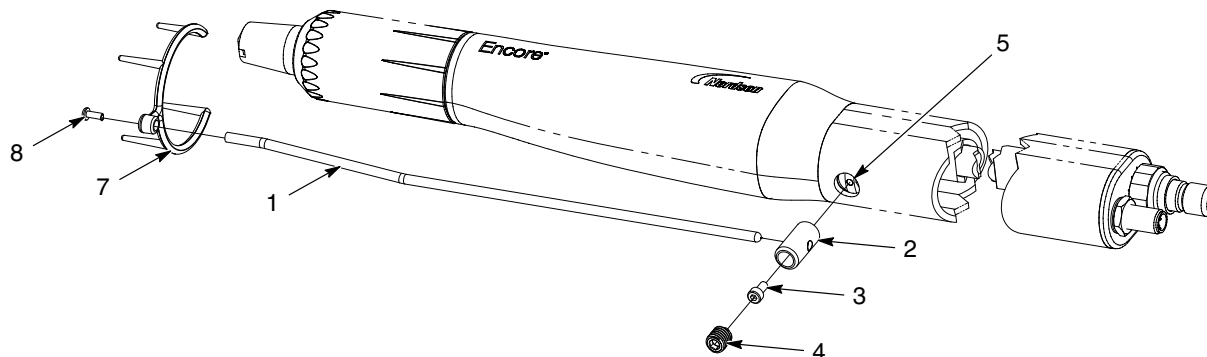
Installation du collecteur d'ions – Pistolet à fixation sur tube
